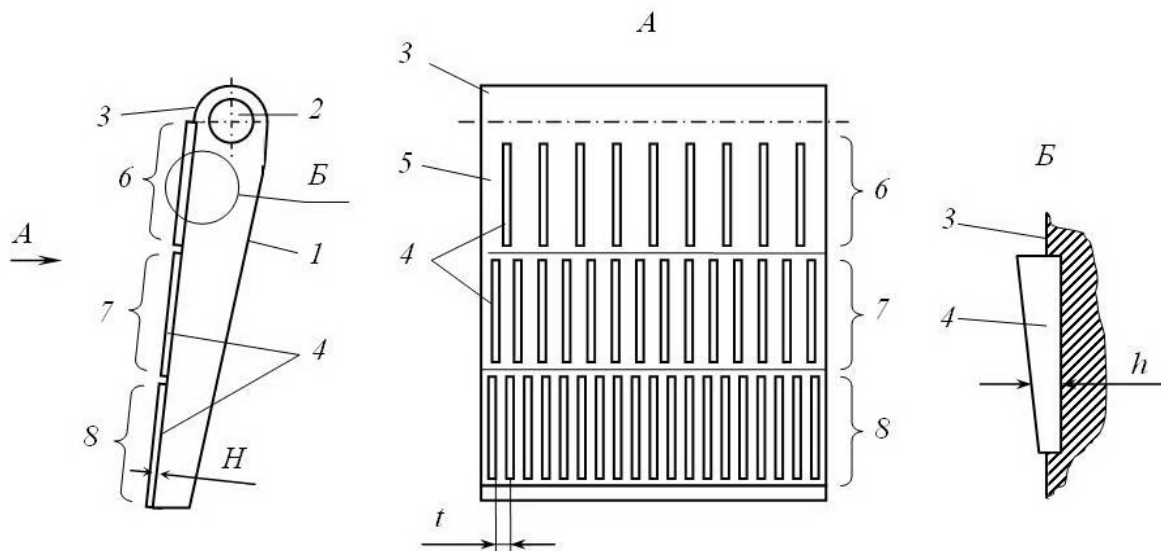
Схема рухомої щоки щокрової дробарки [1]
